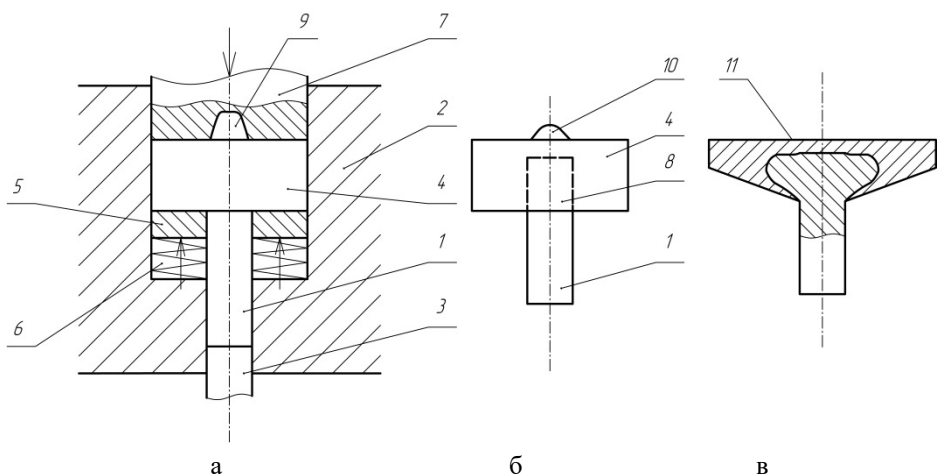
Схема сборки металлических заготовок (а), сборная заготовка (б) и полученное изделие (в): 1 – стержневая заготовка; 2 – матрица; 3 – выталкиватель; 4 – головная заготовка; 5 – упорная плита; 6 – упругий элемент; 7 – пуансон; 8 – внедряемая часть стержневой заготовки; 9 – компенсационная полость; 10 – бобышка; 11 – составное изделие
